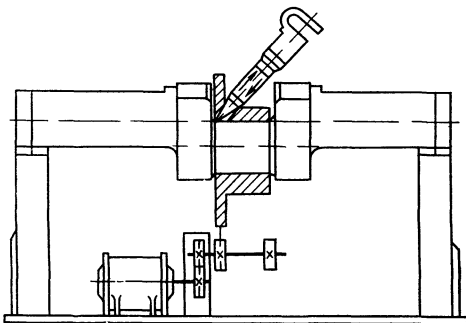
Кинематическая схема чеканочного приспособления для внестаночного упрочнения галтелей прямых и коленчатых валов
